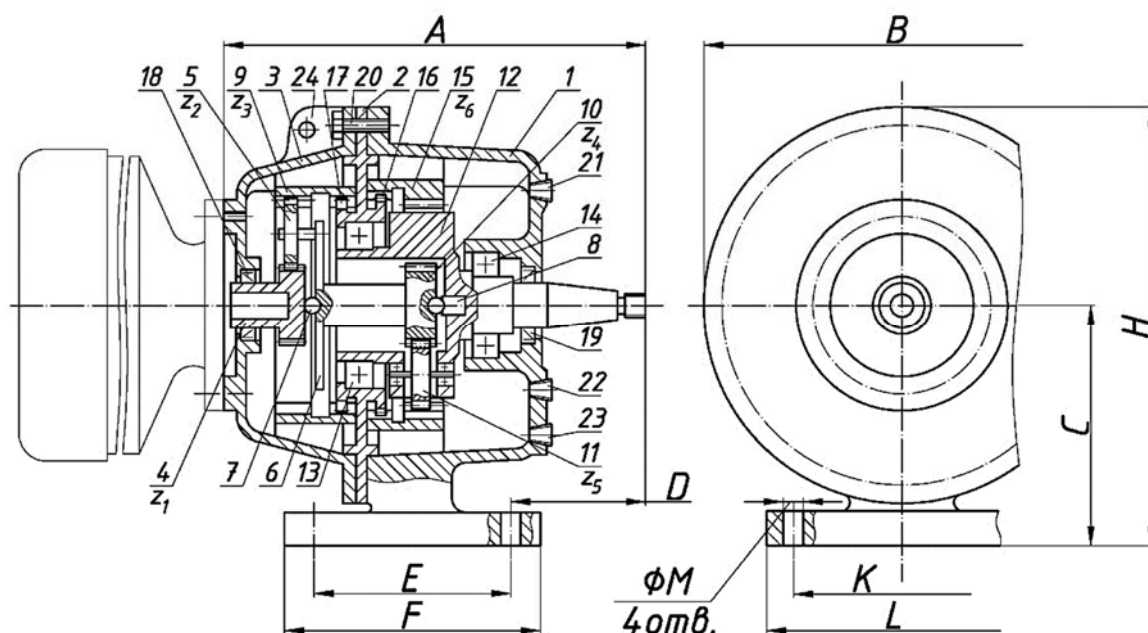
Планетарный двухступенчатый редуктор
